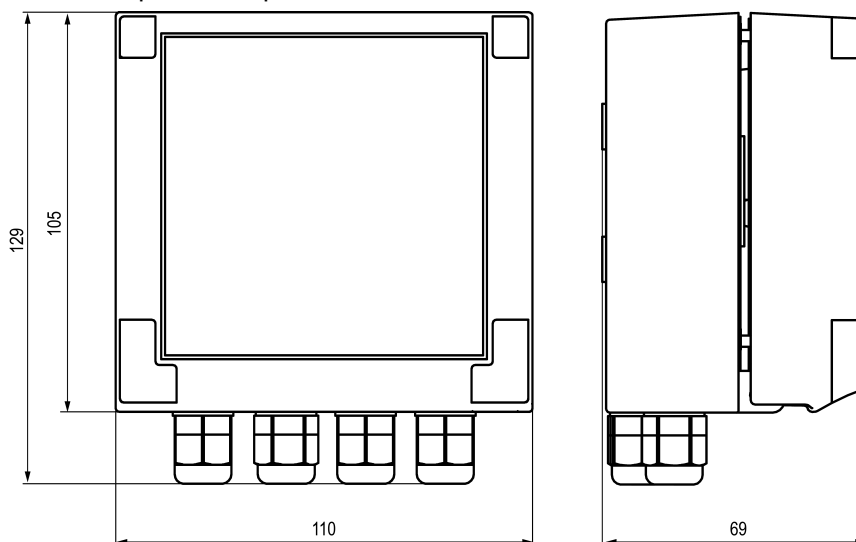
Габаритные размеры прибора в корпусе Н
